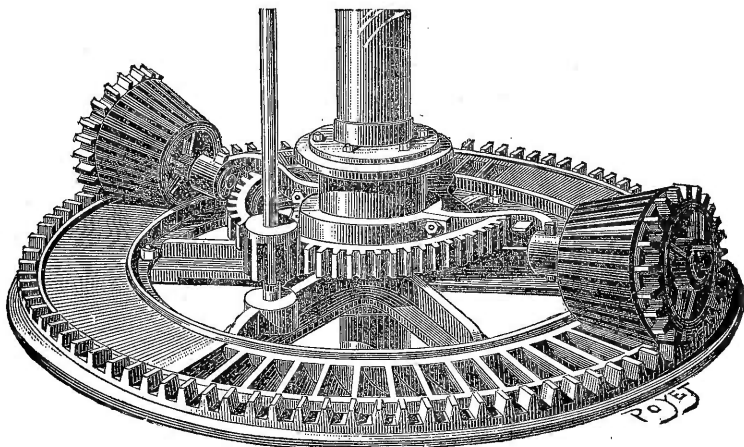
Vue d'ensemble d'un distributeur à papillons de la turbine Fontaine.
